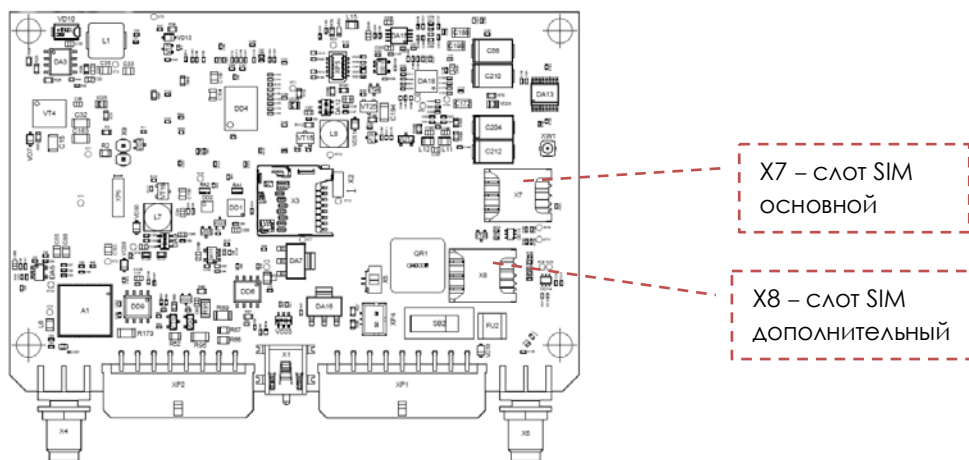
Расположение слотов для основной и дополнительной SIM-карт
